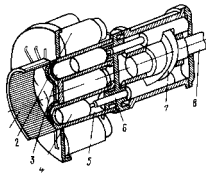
Схема двигателя Стирлинга двойного действия с косой шайбой
